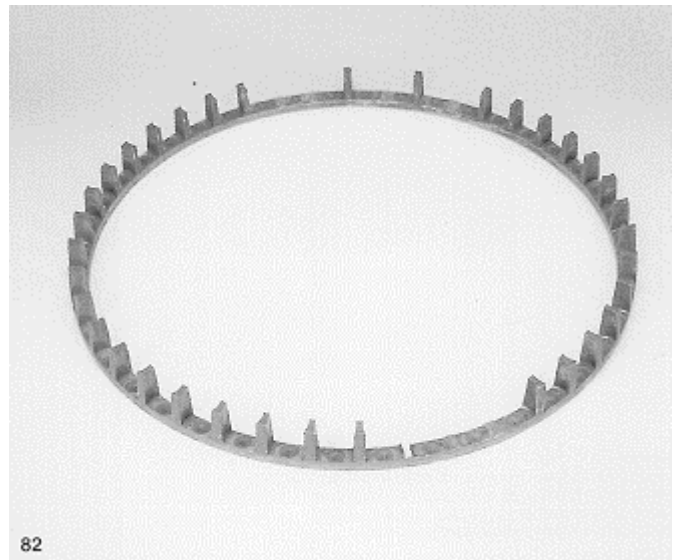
Сепаратор сферического роликоподшипника. В углублениях образовались усталостные трещины.
